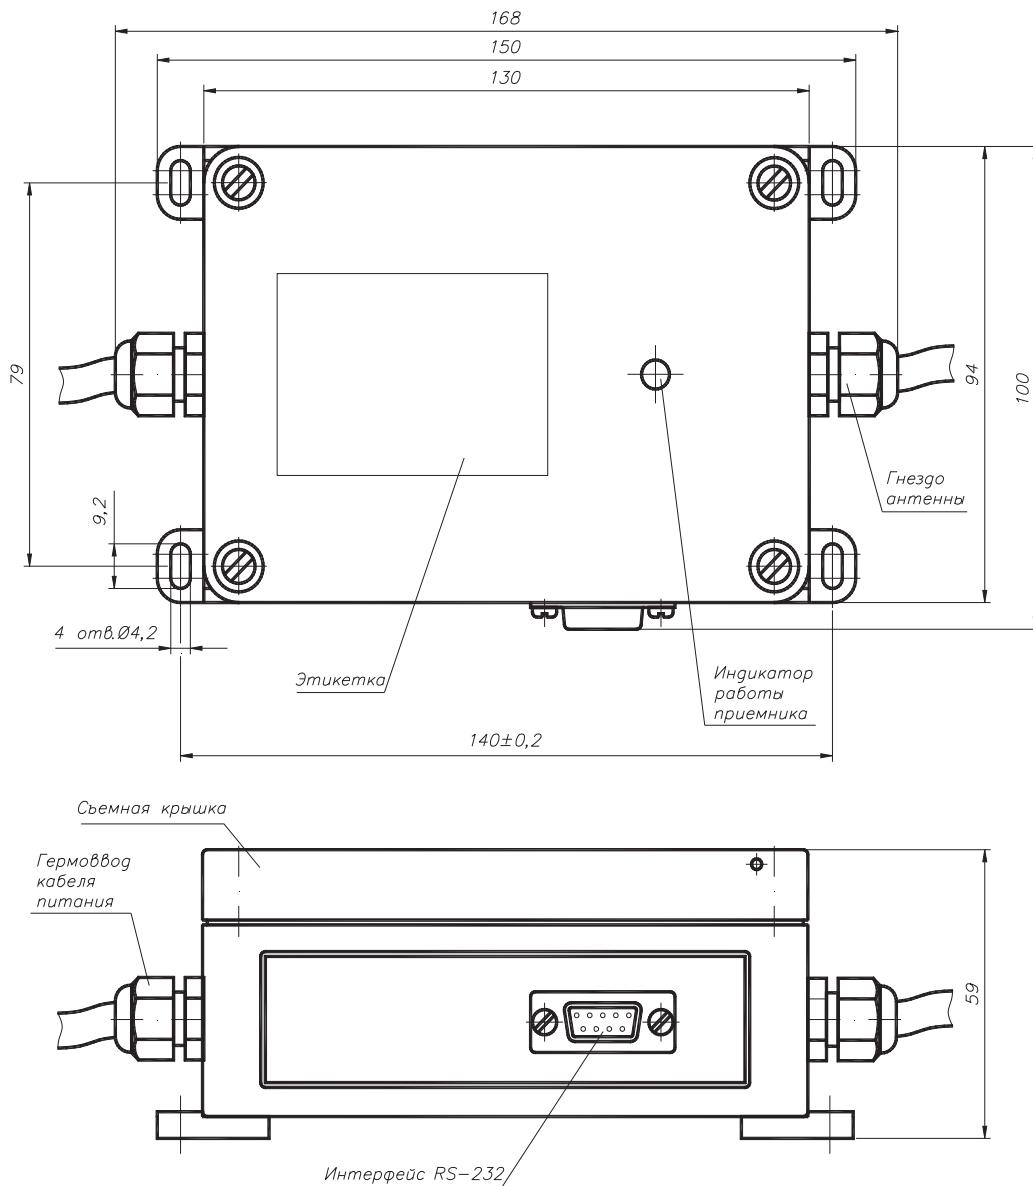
Габаритные и установочные размеры УССВ
